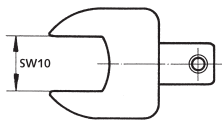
Mauleinsatz SW10 für Montage- und Drehmomentschlüssel Typ 1300A123
